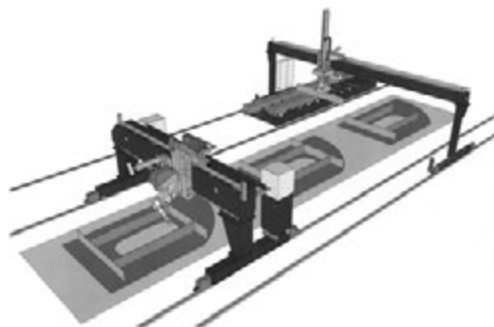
Комплекс механизированной сборки и роботизированной сварки панелей
